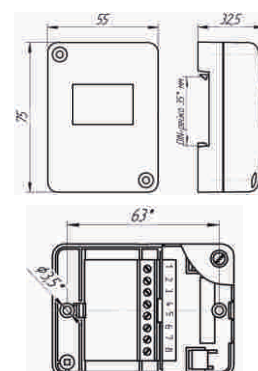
Габаритные и установочные размеры контроллера считывателя.
